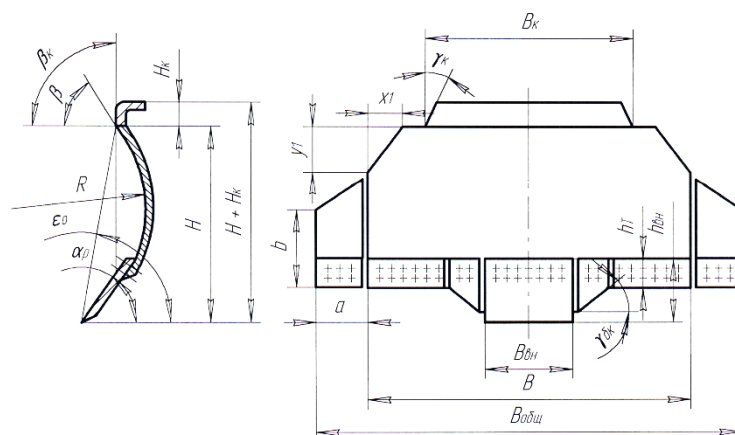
Схема бульдозерного отвала с выступающим средним ножом, боковыми косынками, ножами-уширителями и скосами
